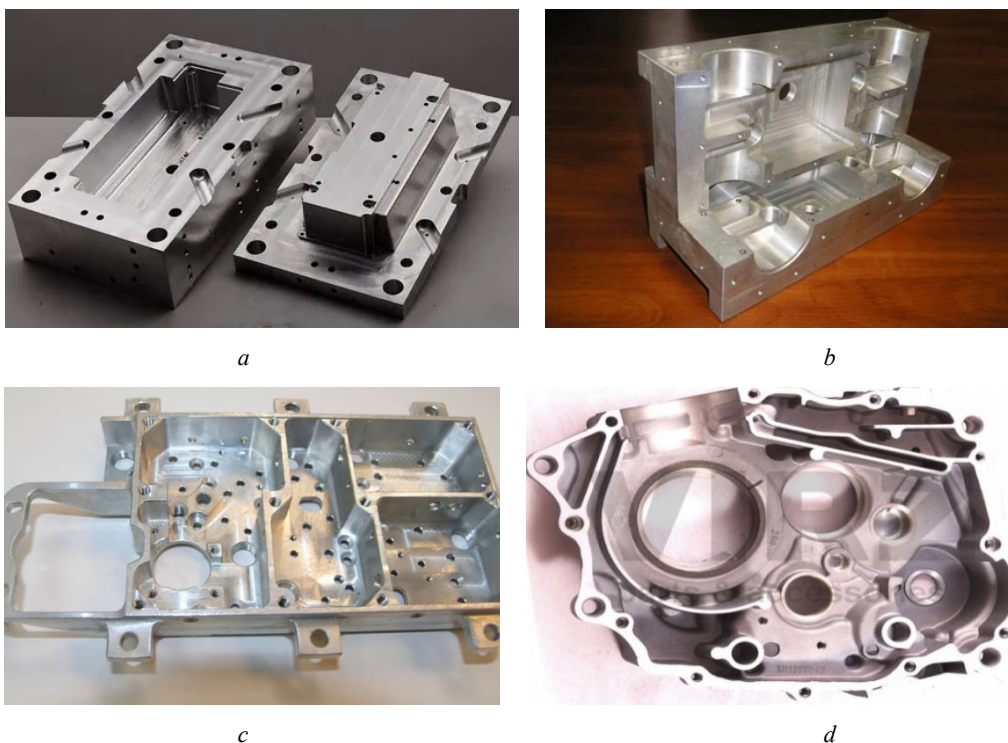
Примеры корпусных (a, b) и плоских (c, d) деталей с большим количеством отверстий
